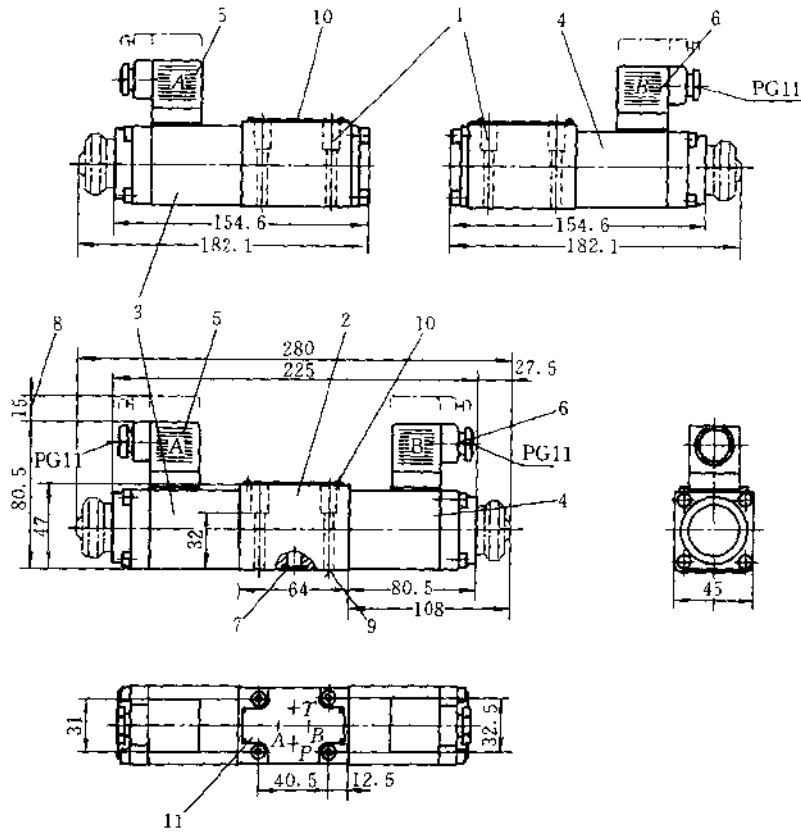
4WRA6 型直动式比例换向阀外形尺寸
